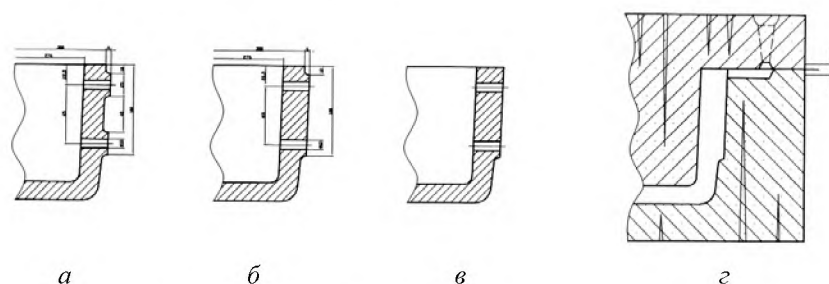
Эскиз детали «корпус» из чугуна СЧ15:
